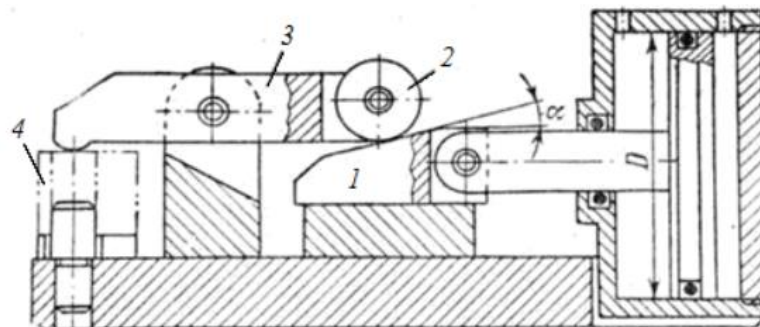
Застосування клинового затискного пристрою для закріплення заготовки
